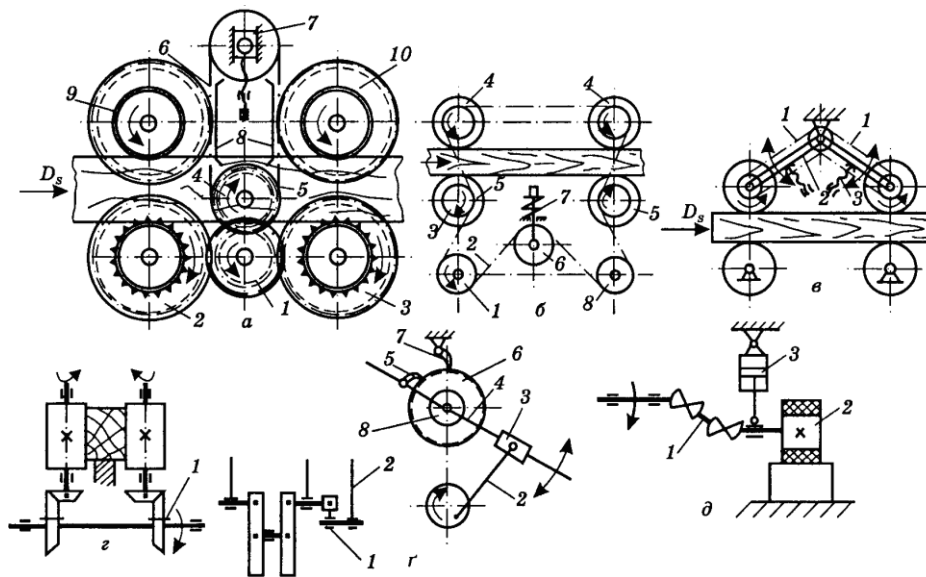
Привод подавальних вальців: а – пилорами з безперервною подачею: 1 – центральна шестірня; 2, 3 – зубчасті колеса; 4 – шестірня; 5 – ведуча зірочка; 6 – ланцюг; 7 – натягувальний блок; 8 – напрямні; 9, 10 – зірочки; б – рейсмусового верстата: 1 – ведуча зірочка; 2 – ланцюг; 3 – ведені зірочки; 4, 5 – вали (верхні, нижні); 6 – натяжний блок; 7 – пружина; 8 – напрямний блок; в – прирізного круглопилкового верстата: 1 – короткі ланцюгові передачі; 2 – коливний супорт; 3 – опори; г – ребрового верстата: 1 – шпонки ковзання; г – пилорами з пульсуючою подачею: 1 – контркривошип; 2 – шатун механізму подачі; 3 – повзун; 4 – коромисло; 5 – фрикційна собачка; 6 – колесо; 7 – гальмуюча собачка; 8 – шестірня; д – чотирибічного поздовжньо-фрезувального верстата: 1 – карданні вали; 2 – подавальні вальці; 3 – пневмоциліндр
